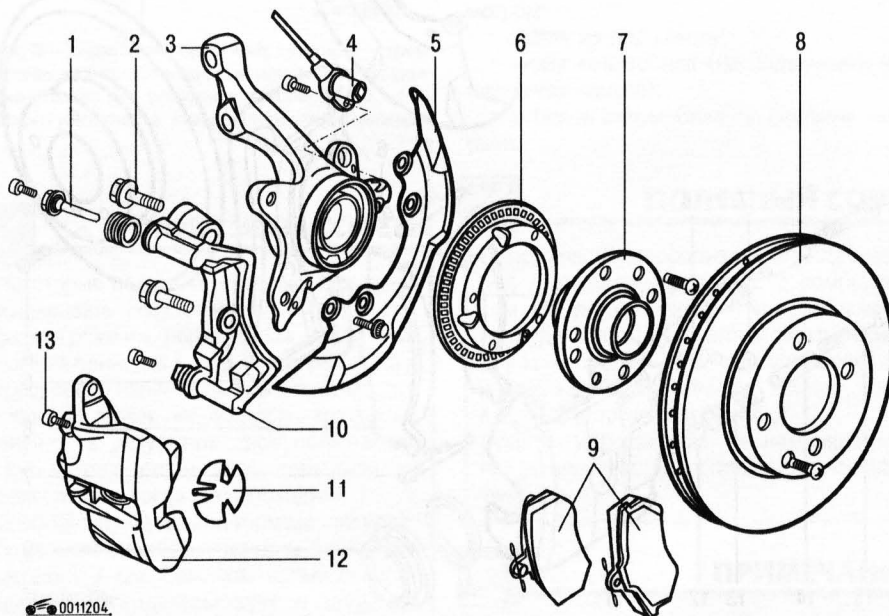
Передний тормозной механизм Girling: 1 – направляющий палец; 2 – болт; 3 – поворотный кулак; 4 – датчик АБС; 5 – защитный кожух; 6 – ротор датчика АБС; 7 – ступица колеса; 8 – вентилируемый диск; 9 – тормозные колодки; 10 – направляющая колодок; 11 – термозащитная пластина; 12 – суппорт; 13 – штуцер прокачки
